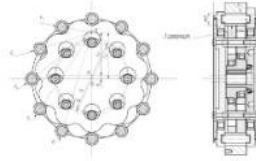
Конструкція модуля планетарно-цивкової передачі з 3 сателітами типу 3К-В
